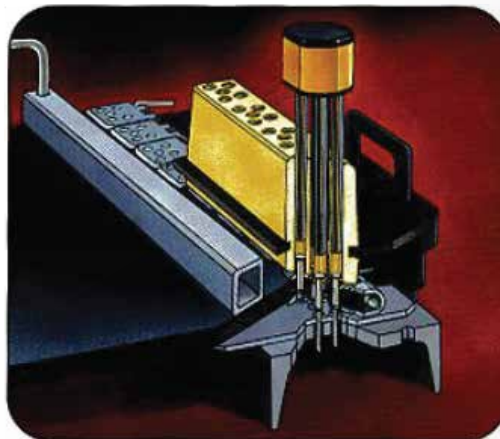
Установка фиксаторов для монтажа соответствующих типоразмеров шарнирных соединений.
